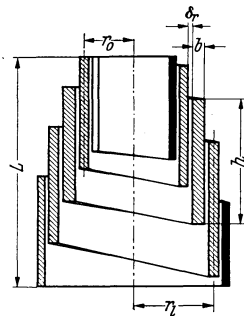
Kegelstumpffeder mit Rechteckquerschnitt.
